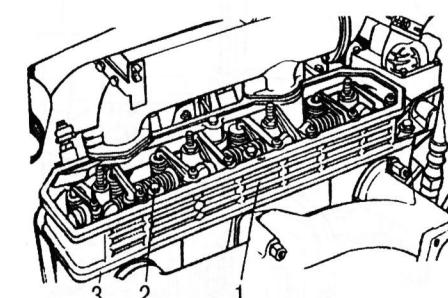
Снятие крышки головки блока цилиндров: 1 – крышка головки блока цилиндров; 2 – болт крепления крышки головки блока цилиндров; 3 – прокладка
